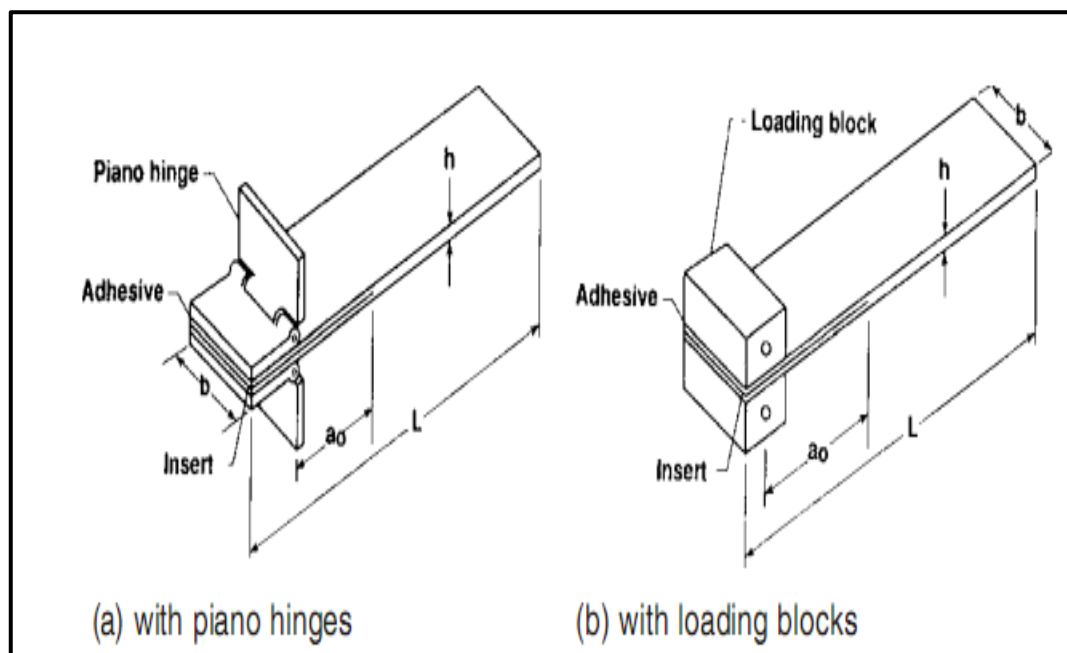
L'éprouvette Double Cantilever Beam (DCB) d'ASTM D 5528 [37].
